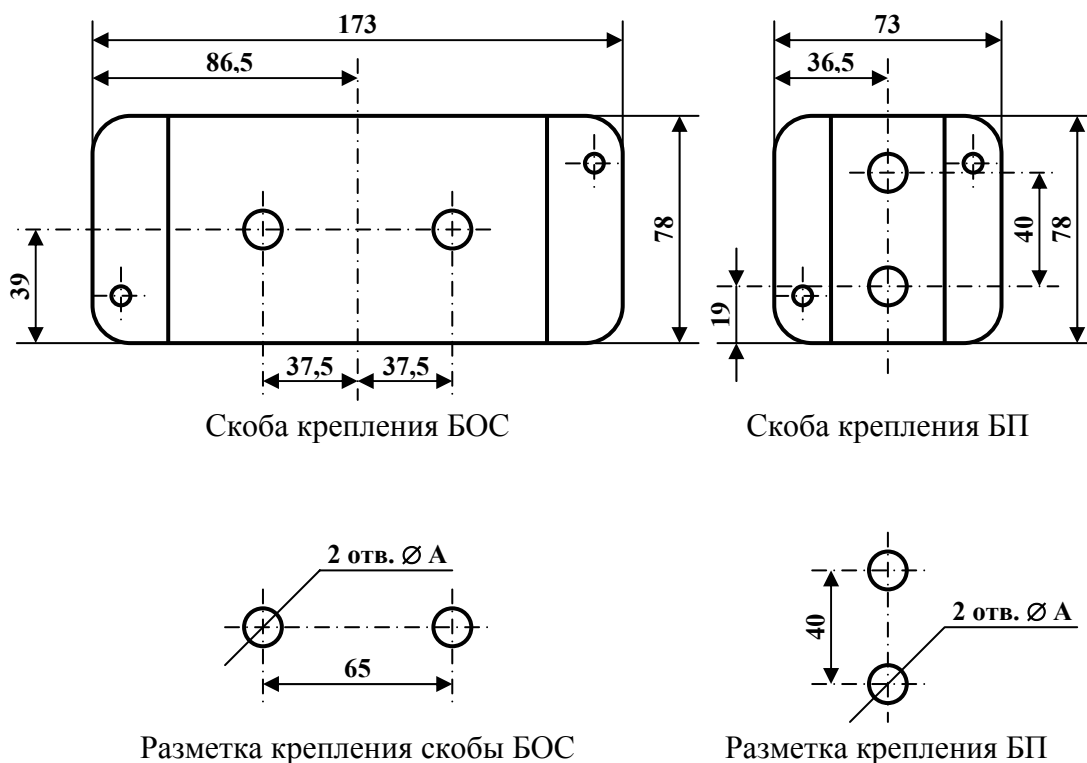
Разметка и габаритные размеры скоб крепления БОС и БП.
